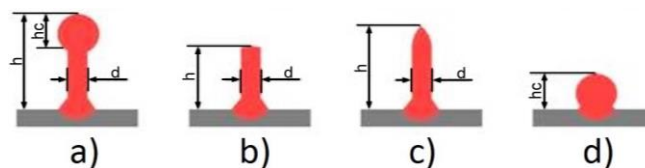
Diferentes geometrias de pinos possíveis com a técnica CMT PIN: a) cabeça abaulada (*ball-head*); b) cabeça cilíndrica (*cylindrical*); c) cabeça pontiaguda (*pike*) e d) impressão (*print*), onde: h – altura do pino; hc – altura/diâmetro da cabeça do pino; d – diâmetro do pino (Fronius, 2008)
